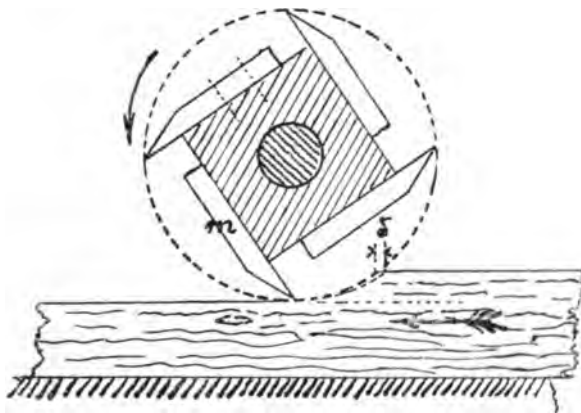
Zeigt die Zuführungsrichtung bei Holzhobelmaschinen.
